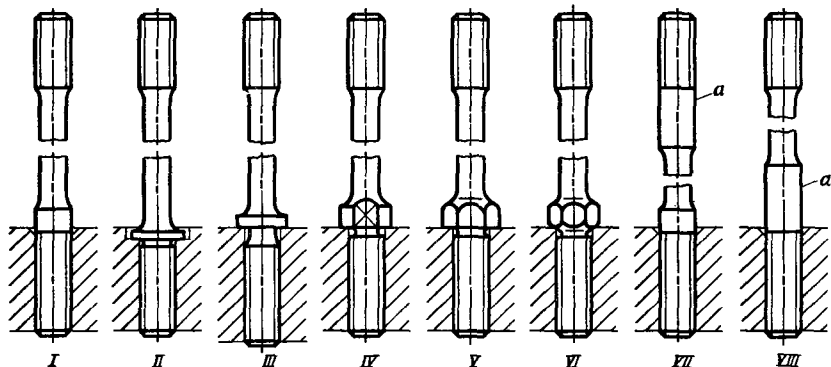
Конструктивные формы шпилек, ввертываемых с упором в торец корпуса
